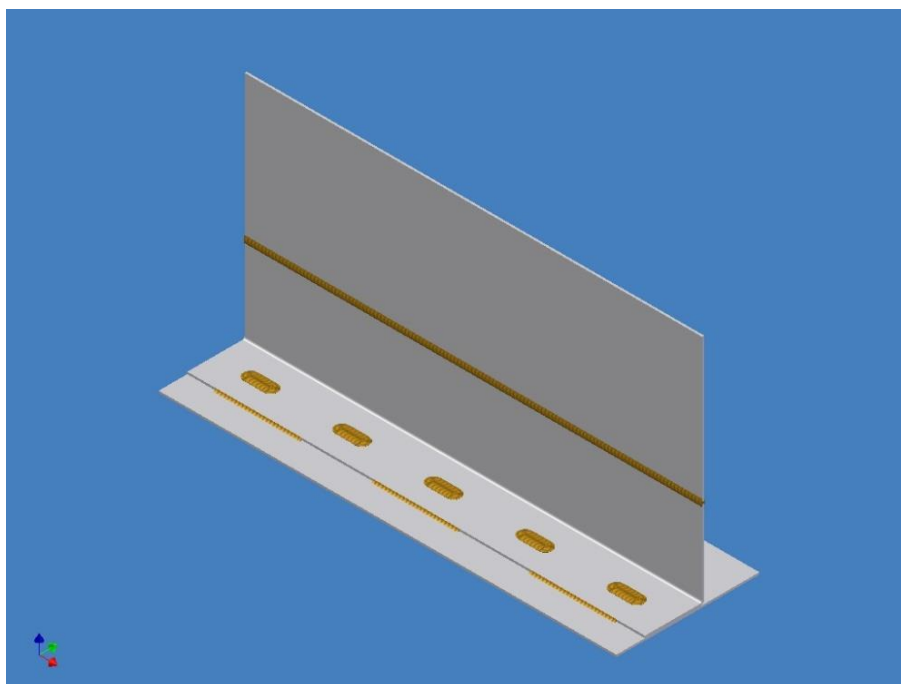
Soldaduras de ojal y ranura. Fuente: TWI
